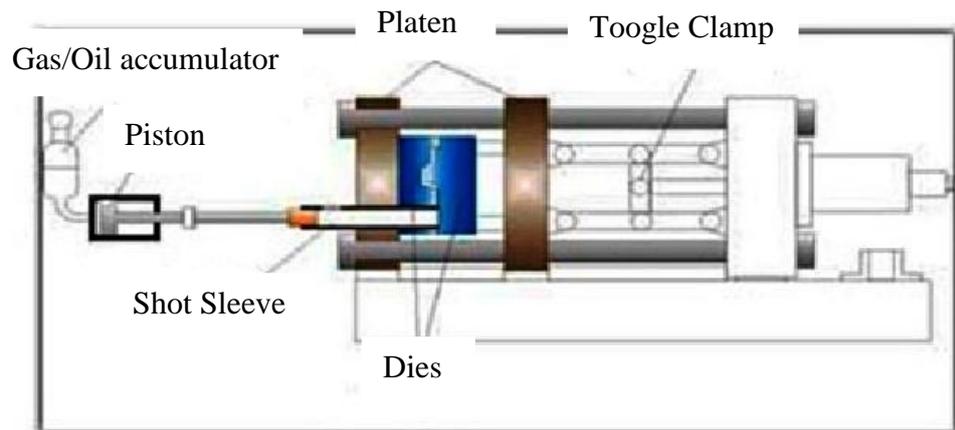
Mesin *Hot Chamber Die Casting* [13].
